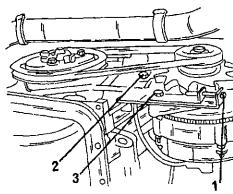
Регулировка натяжения приводного ремня генератора переменного тока.
